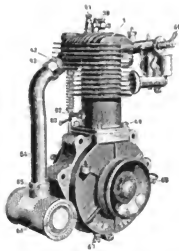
Dürckopp-Einzylindermotor, Seite der Riemenscheibe.
